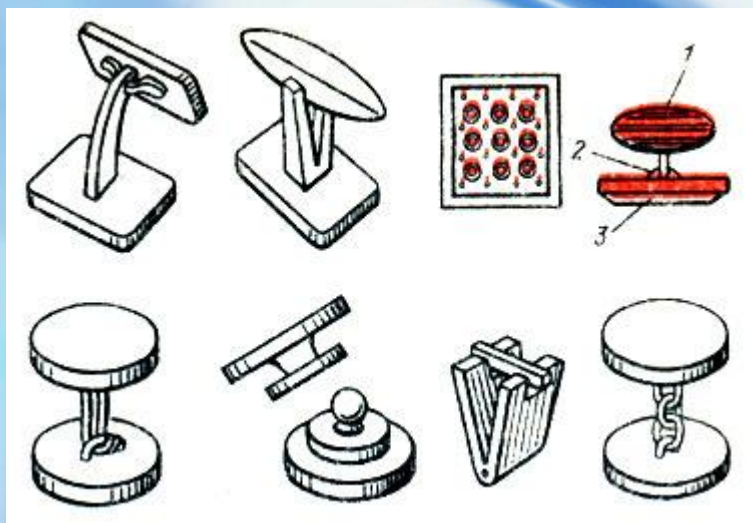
Конструкция запонок: 1 - верхушка; 2 - детали крепления; 3 - застежная часть
